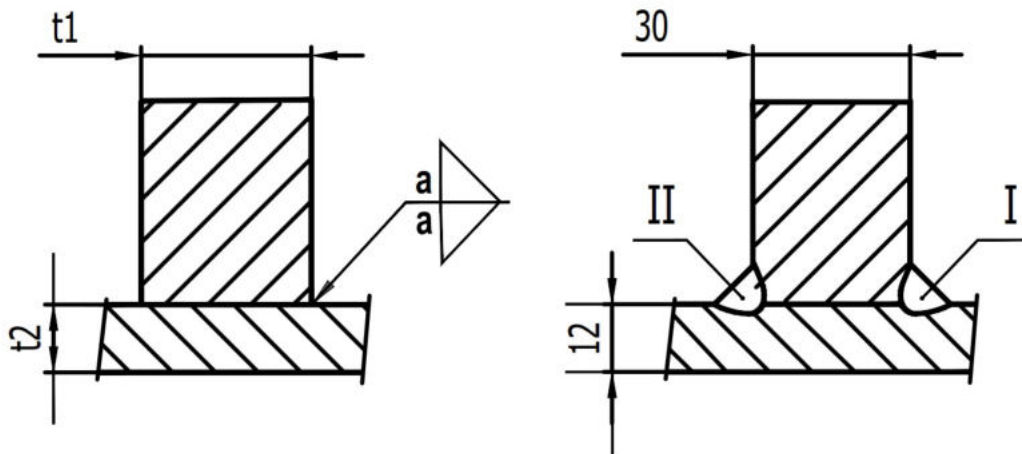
Schéma svaru pro kombinaci svaru P265GH/P265GH
